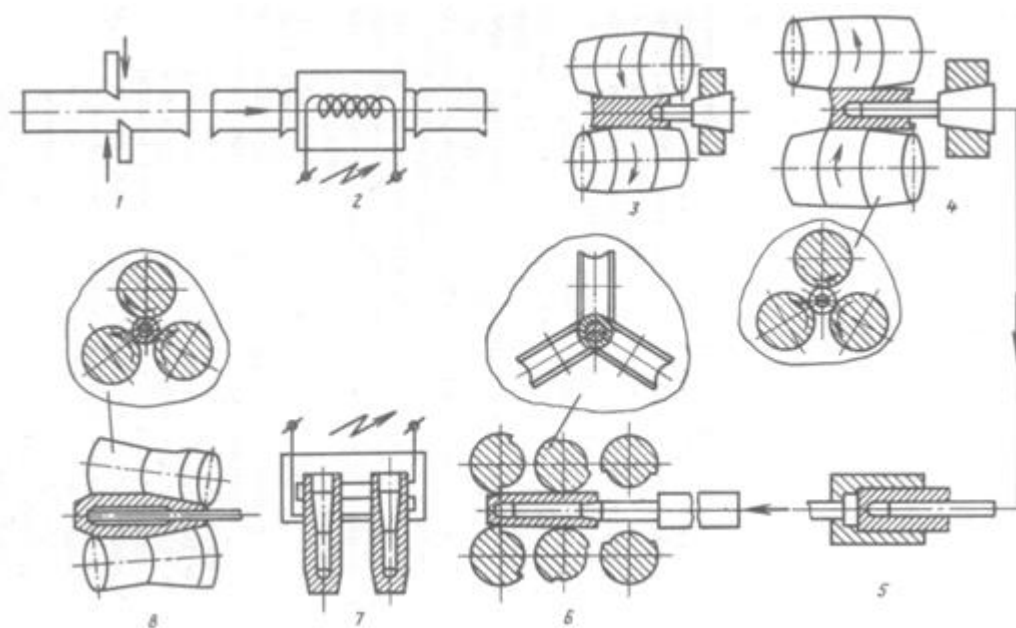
Технологическая схема изготовления полых заготовок диаметром 76...152 мм: 1 – резка прутка на заготовки; 2 – нагрев; 3 – зацентровка заготовки; 4 – винтовая прошивка; 5 – калибровка донной части стакана; 6 – профильная протяжка; 7 – подогрев головной части стакана; 8 – валковый обжим
